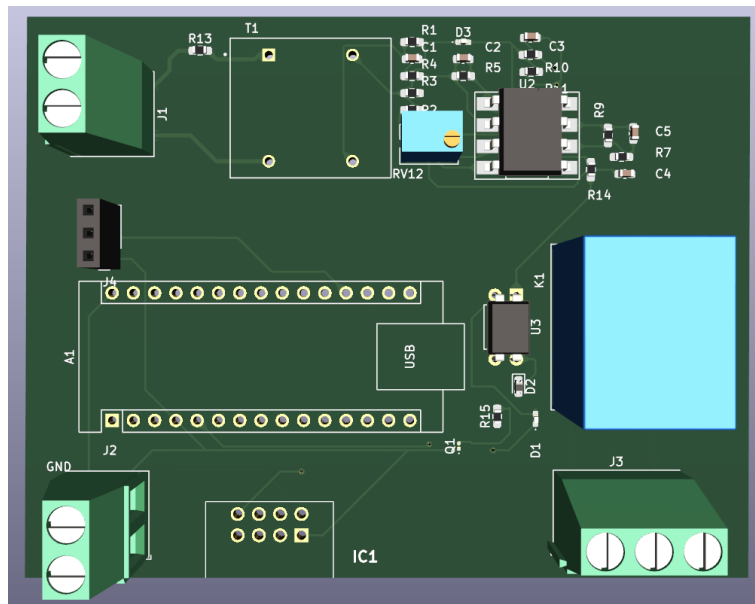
Diseño 3D de PCB Fuente: Autor
